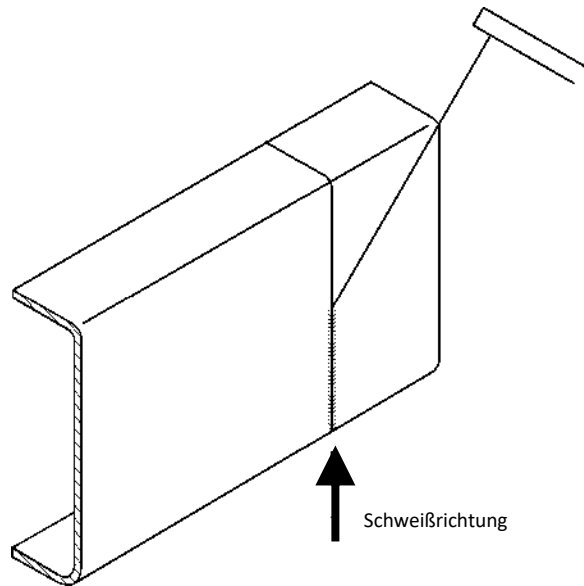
Senkrechte Rahmenschweißung ESC-090
